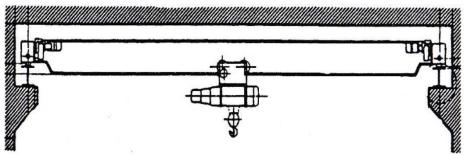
Viga principal de tipo cajón (10) (p. 258)
